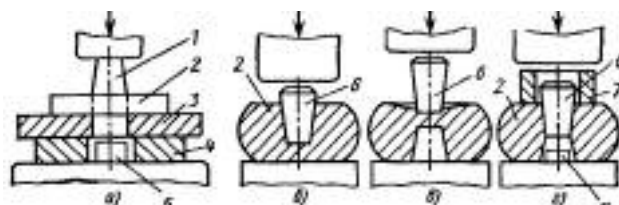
Способы образования отверстий в заготовках на молотах
